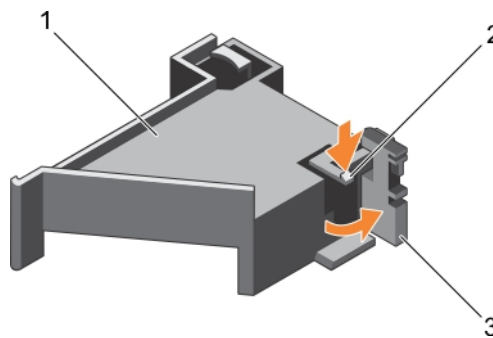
Ouverture et fermeture du loquet du support de carte PCIe
